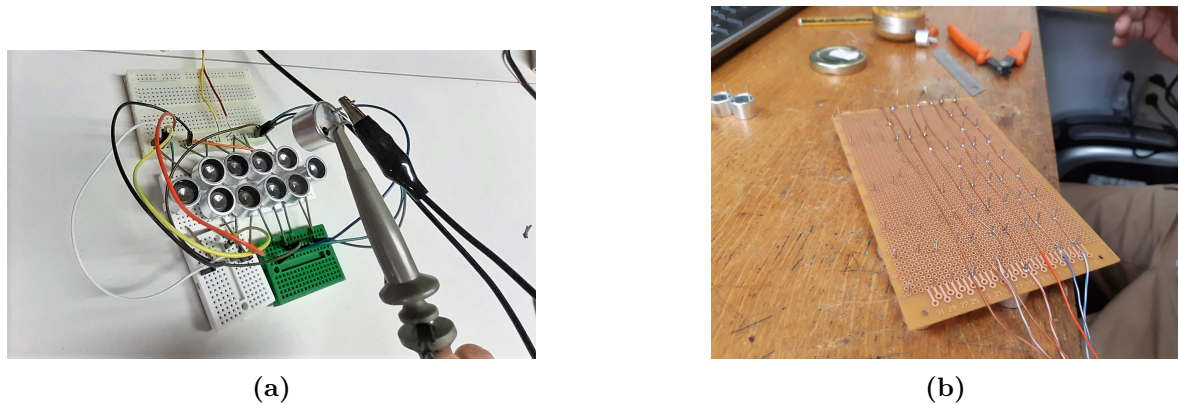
Proceso de construcción: (a) imagen de la primera aproximación y, (b) soldadura de estaño en la PCB.
